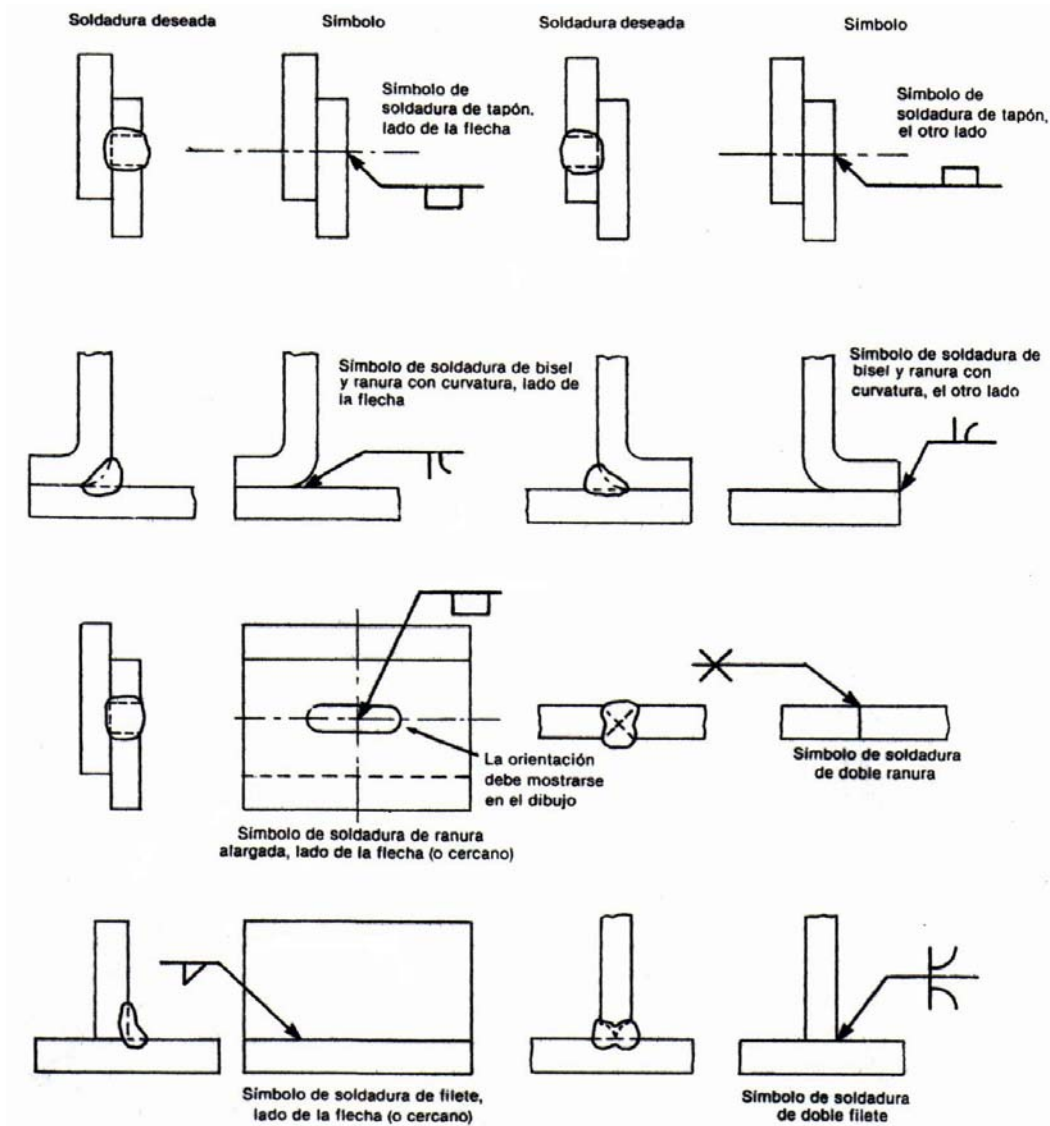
Localización y significado de la flecha en los símbolos de soldadura
